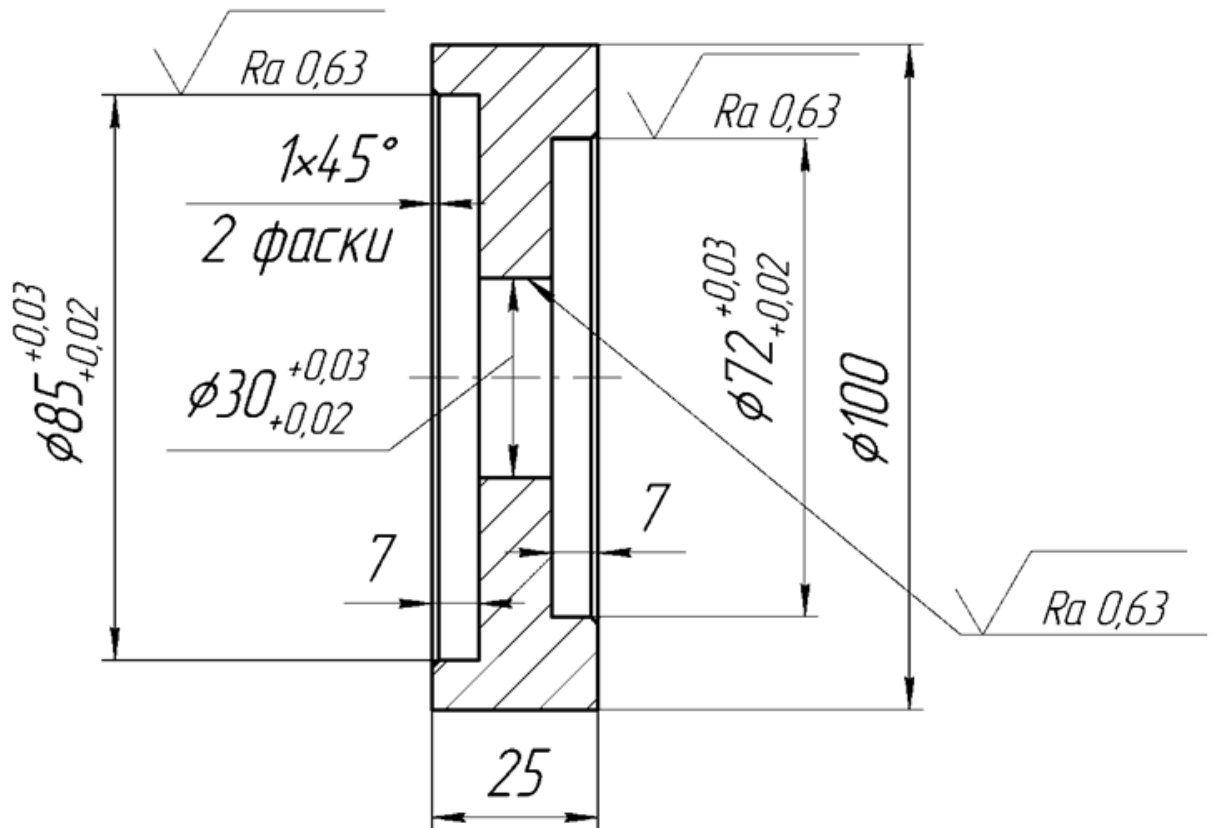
Центрирующее приспособление для сборки деталей клеевого соединения
